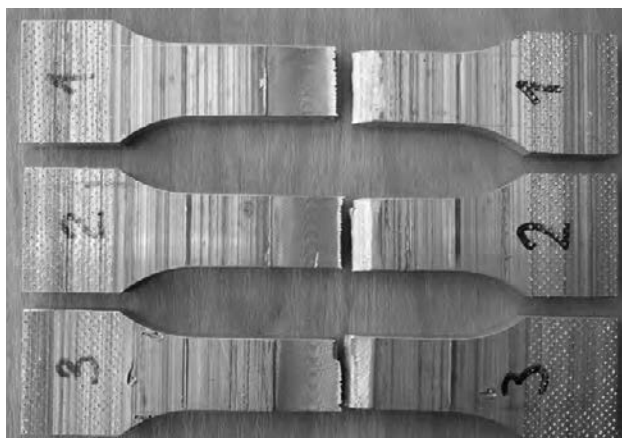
Образцы сварного шва 1, 2 и 3 после проведения испытаний на статическое растяжение
